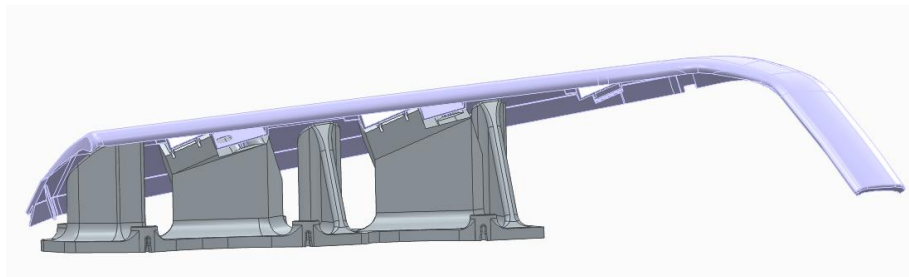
Módulo 1 del utillaje 4 con pieza de trabajo incorporada
